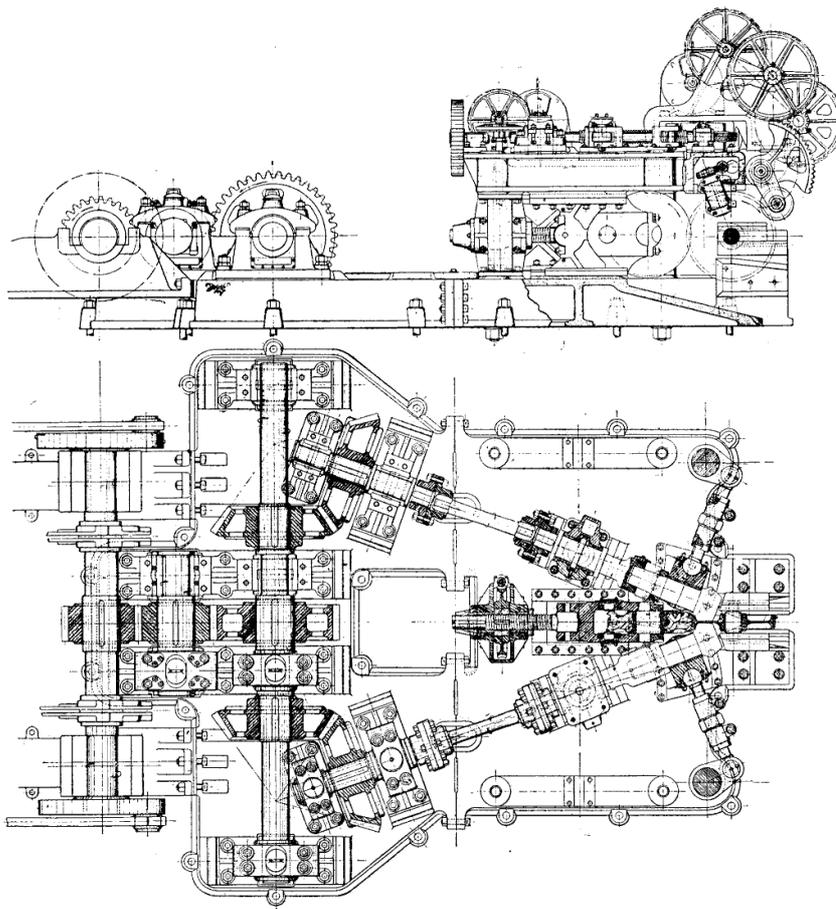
Laminoir Schoen. Élévation et plan-coupe.
